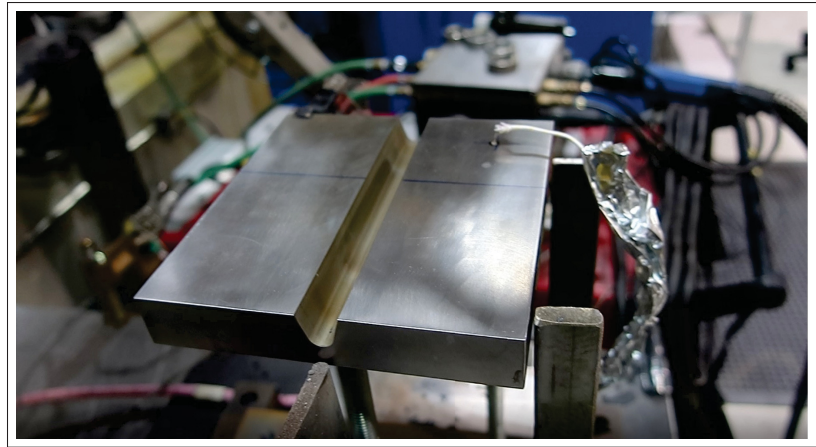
Plaque instrumentée avant le soudage
